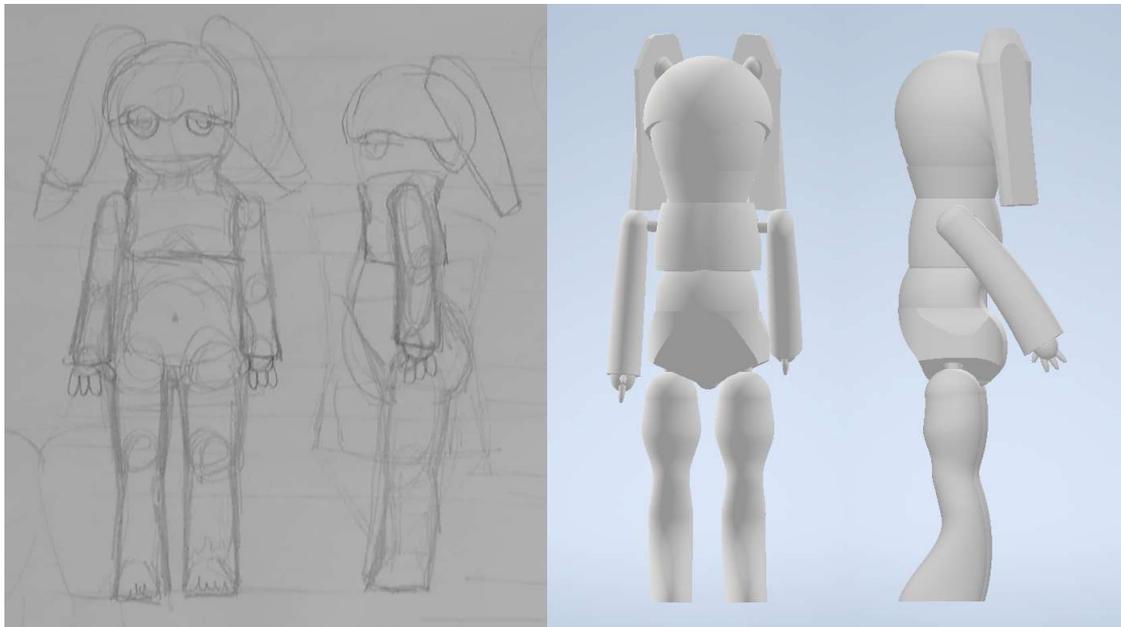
Composición de alzado y perfil del conjunto; bocetado y modelado.
